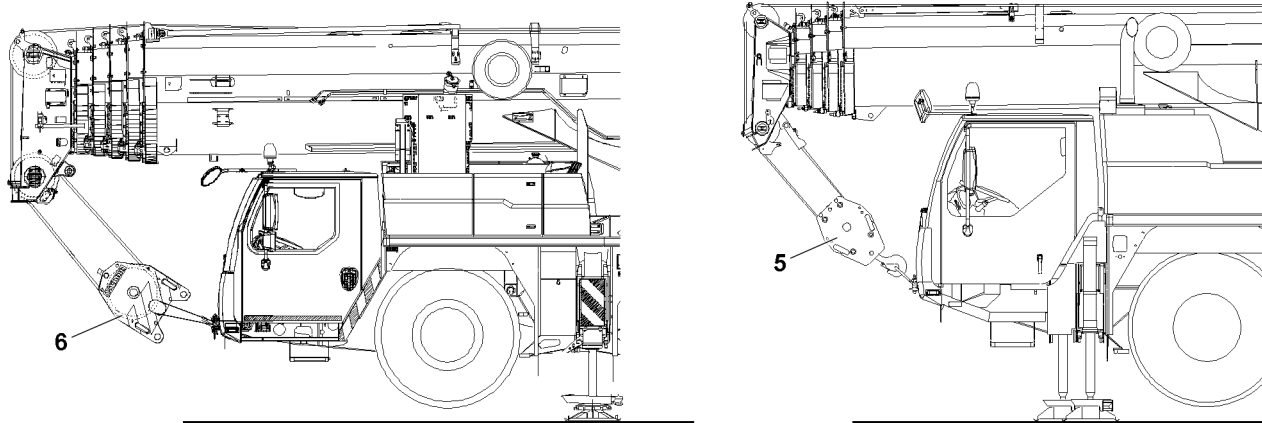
O conjunto de roldanas ou o moitão de gancho está engatado
